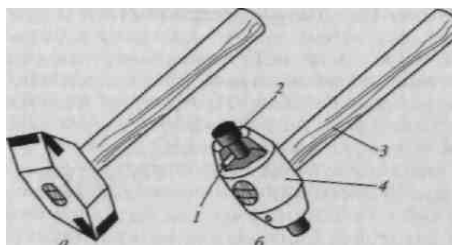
Молотки с мягкими вставками: а - с призматической; б - с цилиндрической: 1 - штифт; 2 - боек; 3 - рукоятка; 4 - корпус
